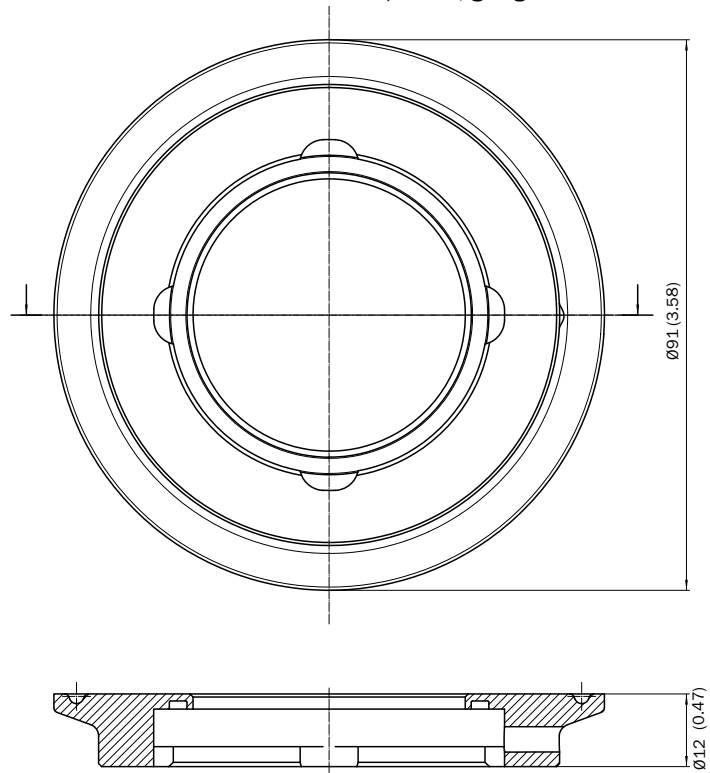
Abmessungen, Montage von Anbaufansch mit M8-Schrauben geeignet für PS=10 bar (150 psi)
